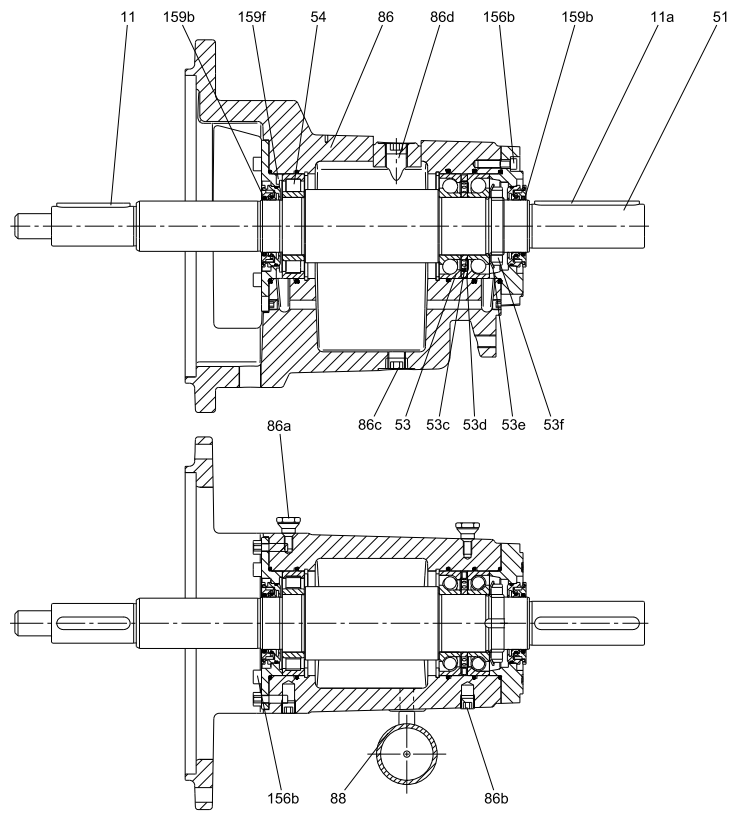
Подшипниковый узел NKG с масляной смазкой
